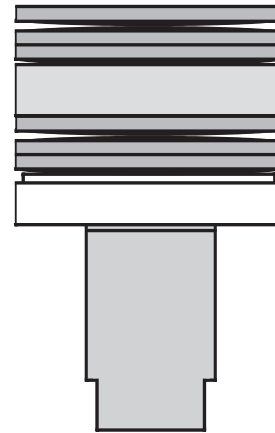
Montaje correcto del adaptador de válvula al actuador EL565
